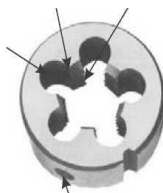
Зовнішній вигляд плашки: 1 – канавка для відведення стружки; 2 – забірна частина; (для нарізання неповного витка); 3 – калібрувальна частина (для нарізання повного витка); 4 – отвір для стопоріння
